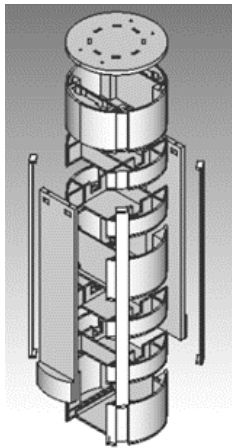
Конструкция аппарата-деплойера (exploded view)
